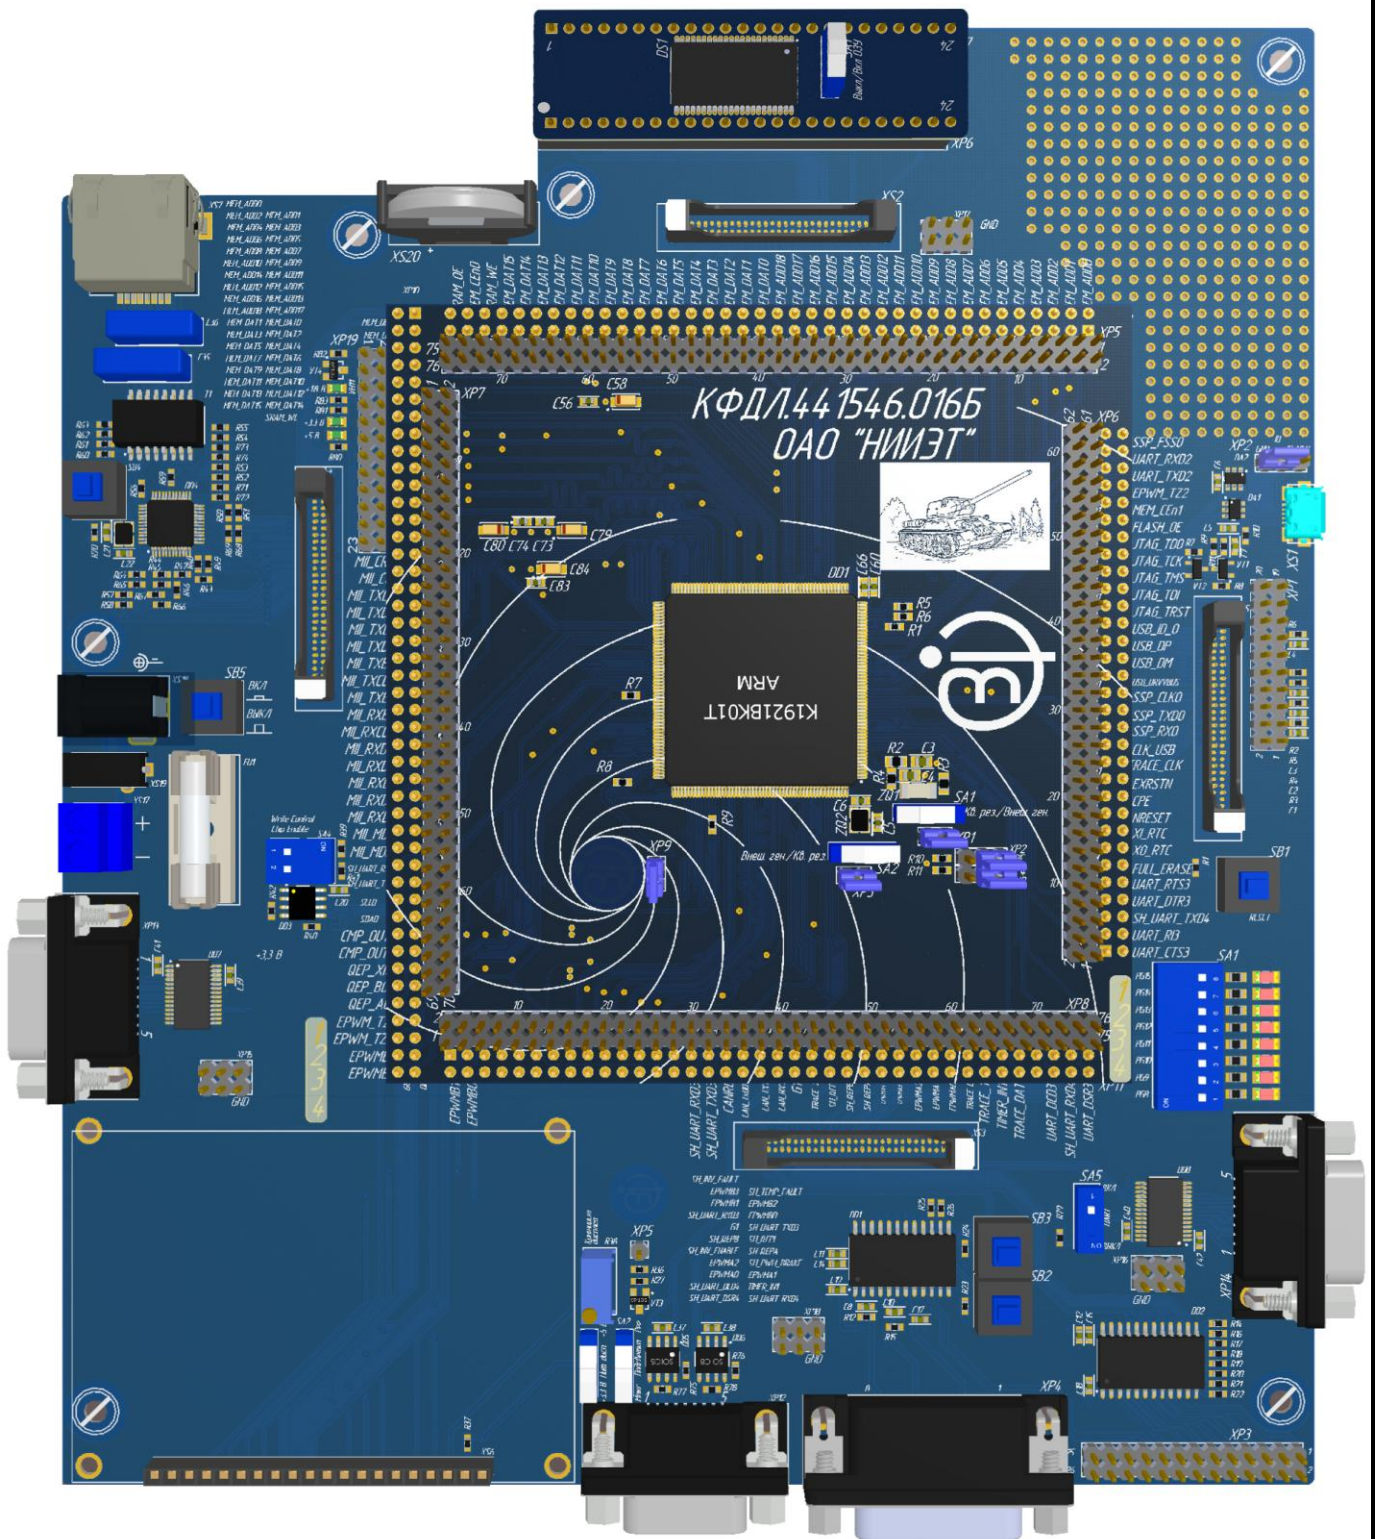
Общий вид платы макетно-отладочной в сборе
